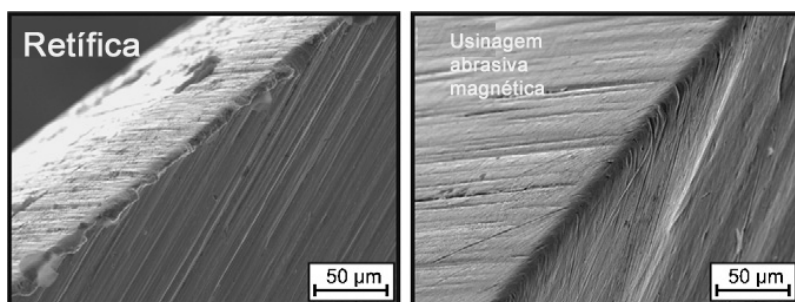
Aresta da broca antes e depois da usinagem abrasiva magnética [32]
